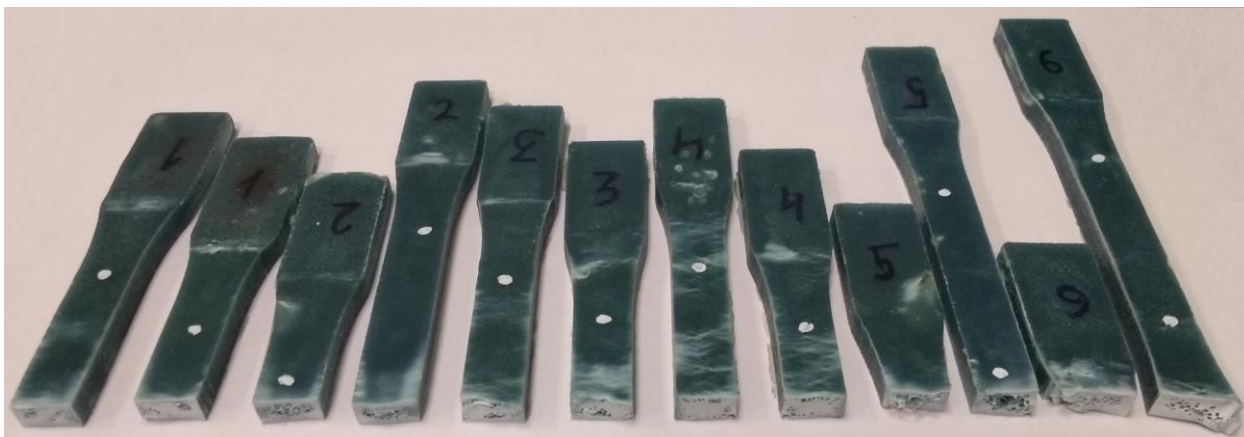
Поверхности разрыва образцов, изготовленных из клея Plexus MA420
